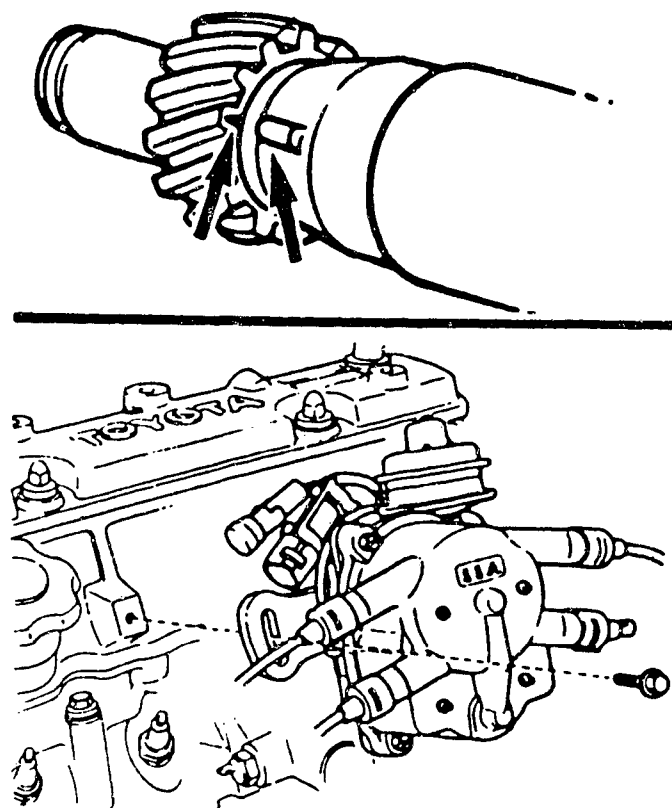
Einbau des Zündverters im Motor 1-S. Oben: Die Markierungen an Verteilerwelle und Gehäuse müssen fluchten – Unten: Beim Einführen des Zündverters muss die Mutter des Befestigungsflansches mit der Bohrung im Nockenwellengehäuse fluchten.
